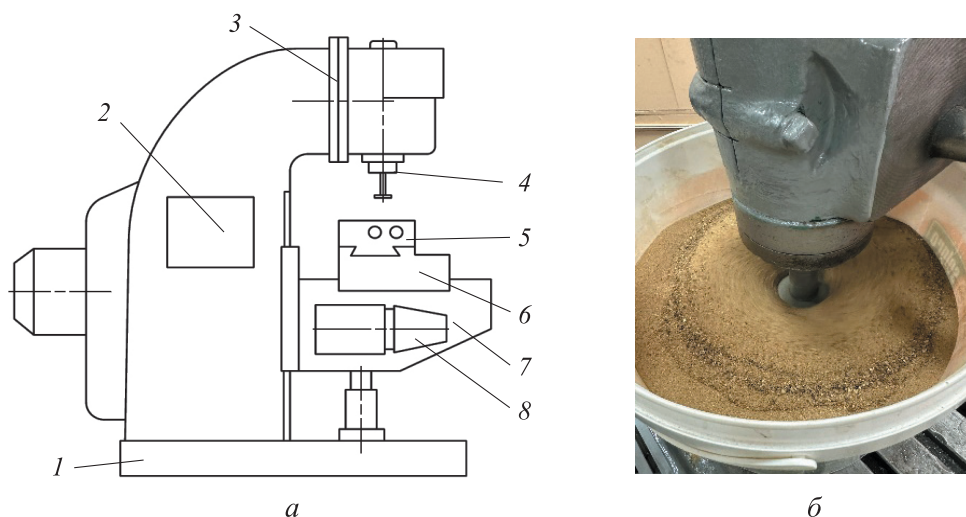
Схема (а) и внешний вид (б) фрезерного станка для имитационных испытаний: 1 — станина; 2 — коробка скоростей; 3 — поворотная головка; 4 — шпиндель; 5 — рабочий стол; 6 — салазки; 7 — консоль; 8 — коробка подачи
